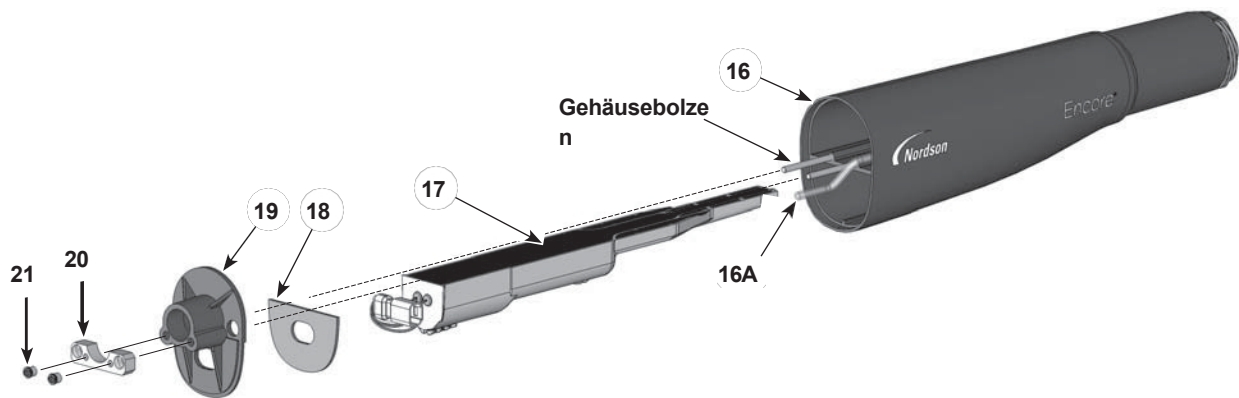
Demontage der Pistole– Austausch des Netzteils
